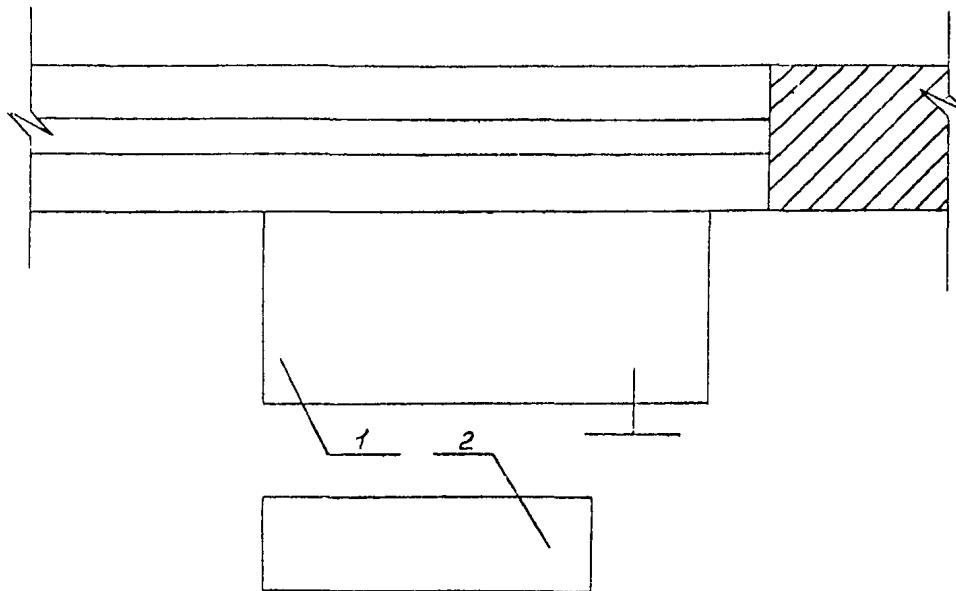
Типовая схема планировки рабочего места разборки и сборки карданных валов
